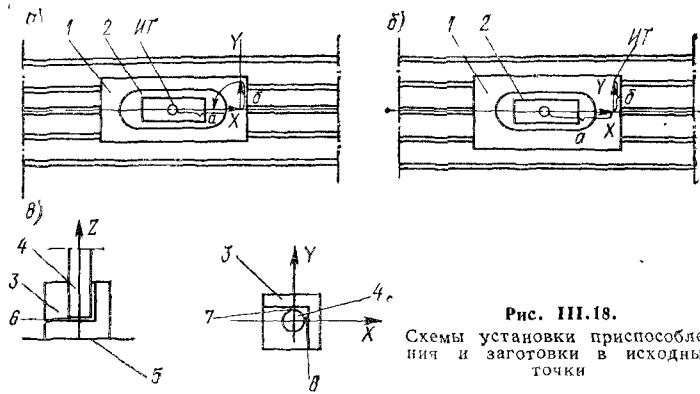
Схемы установки приспособления и заготовки в исходные точки
